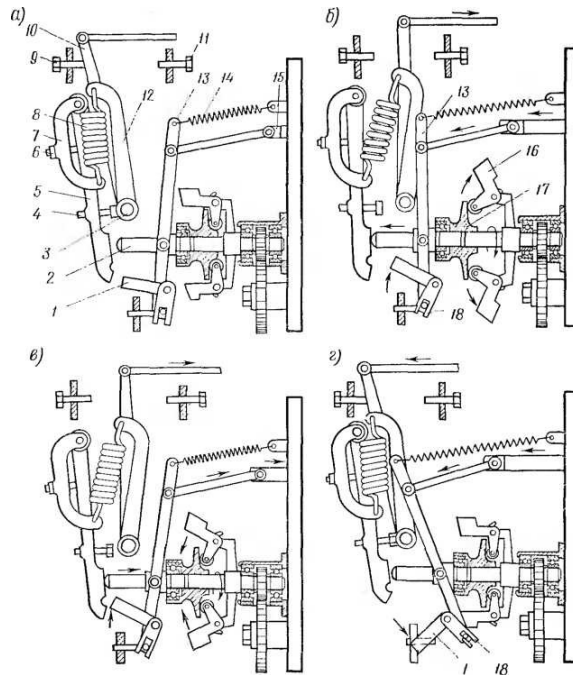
Схема роботи регулятора числа обертів:
